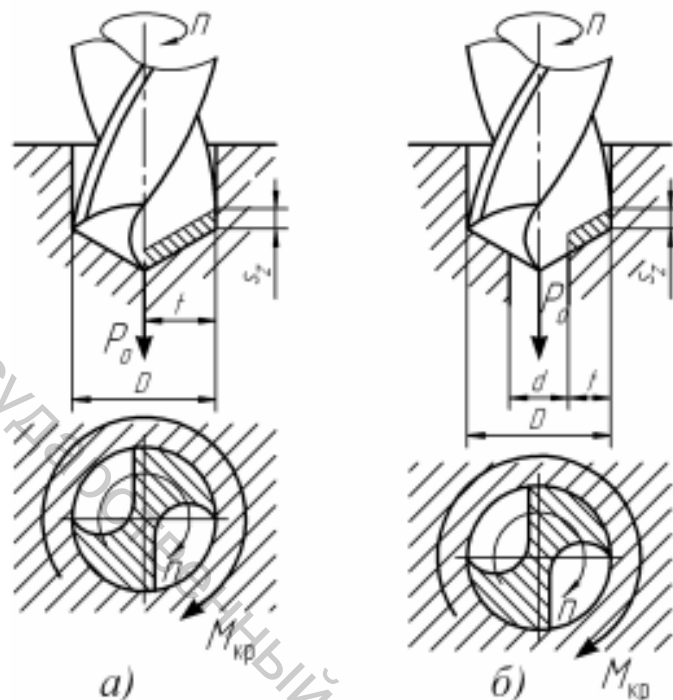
Схема резания: а – сверление; б – рассверливание, зенкерование
